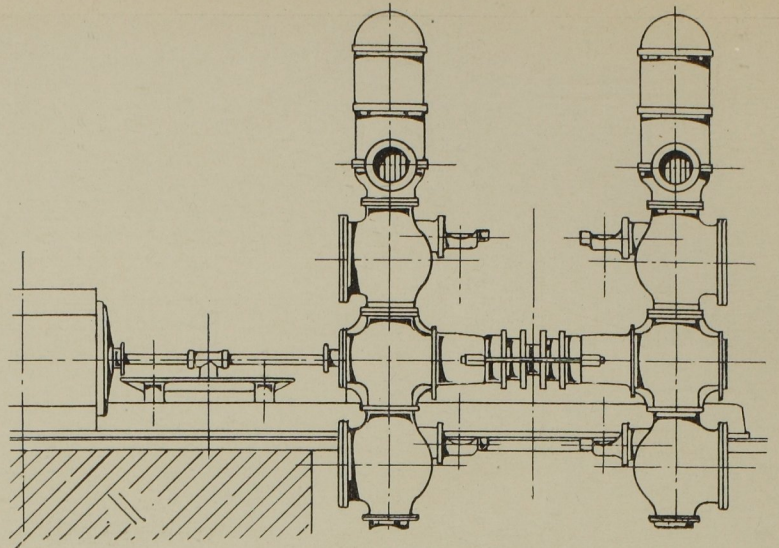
Seitenansicht der Pumpe. Masst. 1:90.
